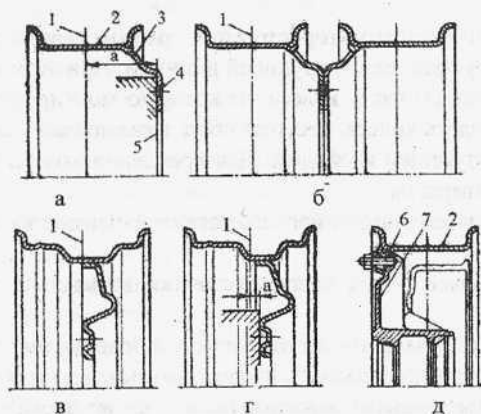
Конструктивные схемы колес: а – одинарного; б – сдвоенного; в – с нулевым вылетом; г – с положительным вылетом; д – бездисковое колесо; 1 – вертикальная ось колеса; 2 – обод; 3 – диск; 4 – крепежное отверстие диска; 5 – центральное отверстие диска; 6 – элемент крепления; 7 – ступица
